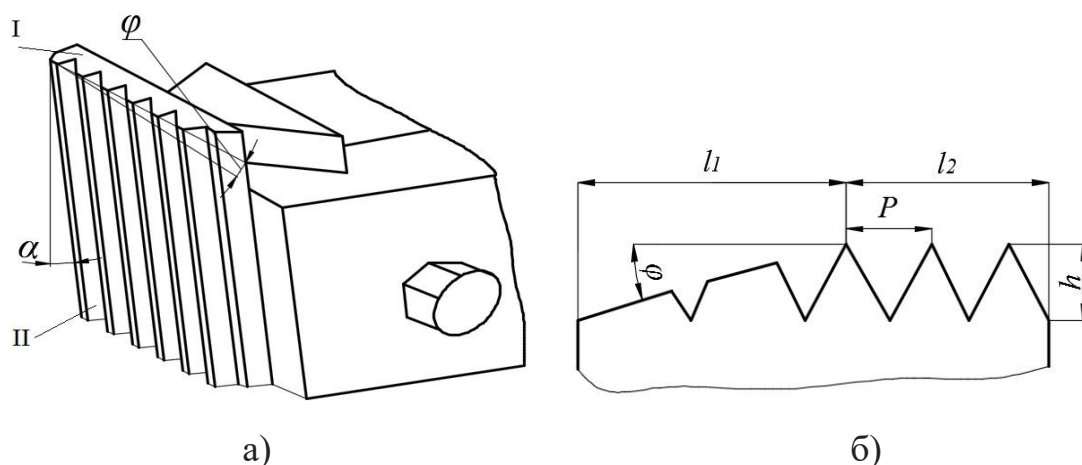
Призматична різьбова гребінка (а) і параметри її робочої частини (б); I - передня поверхня; II - задня поверхня
